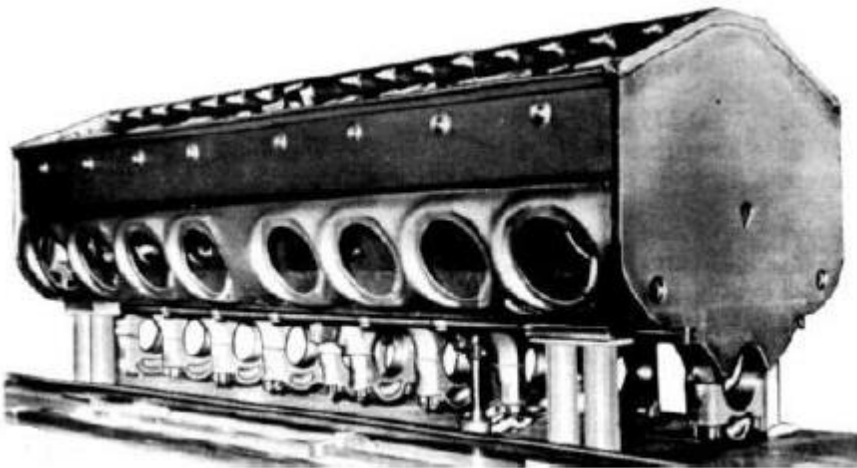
645E3C 16 silindir motor kompleksi, Önden görünüş
